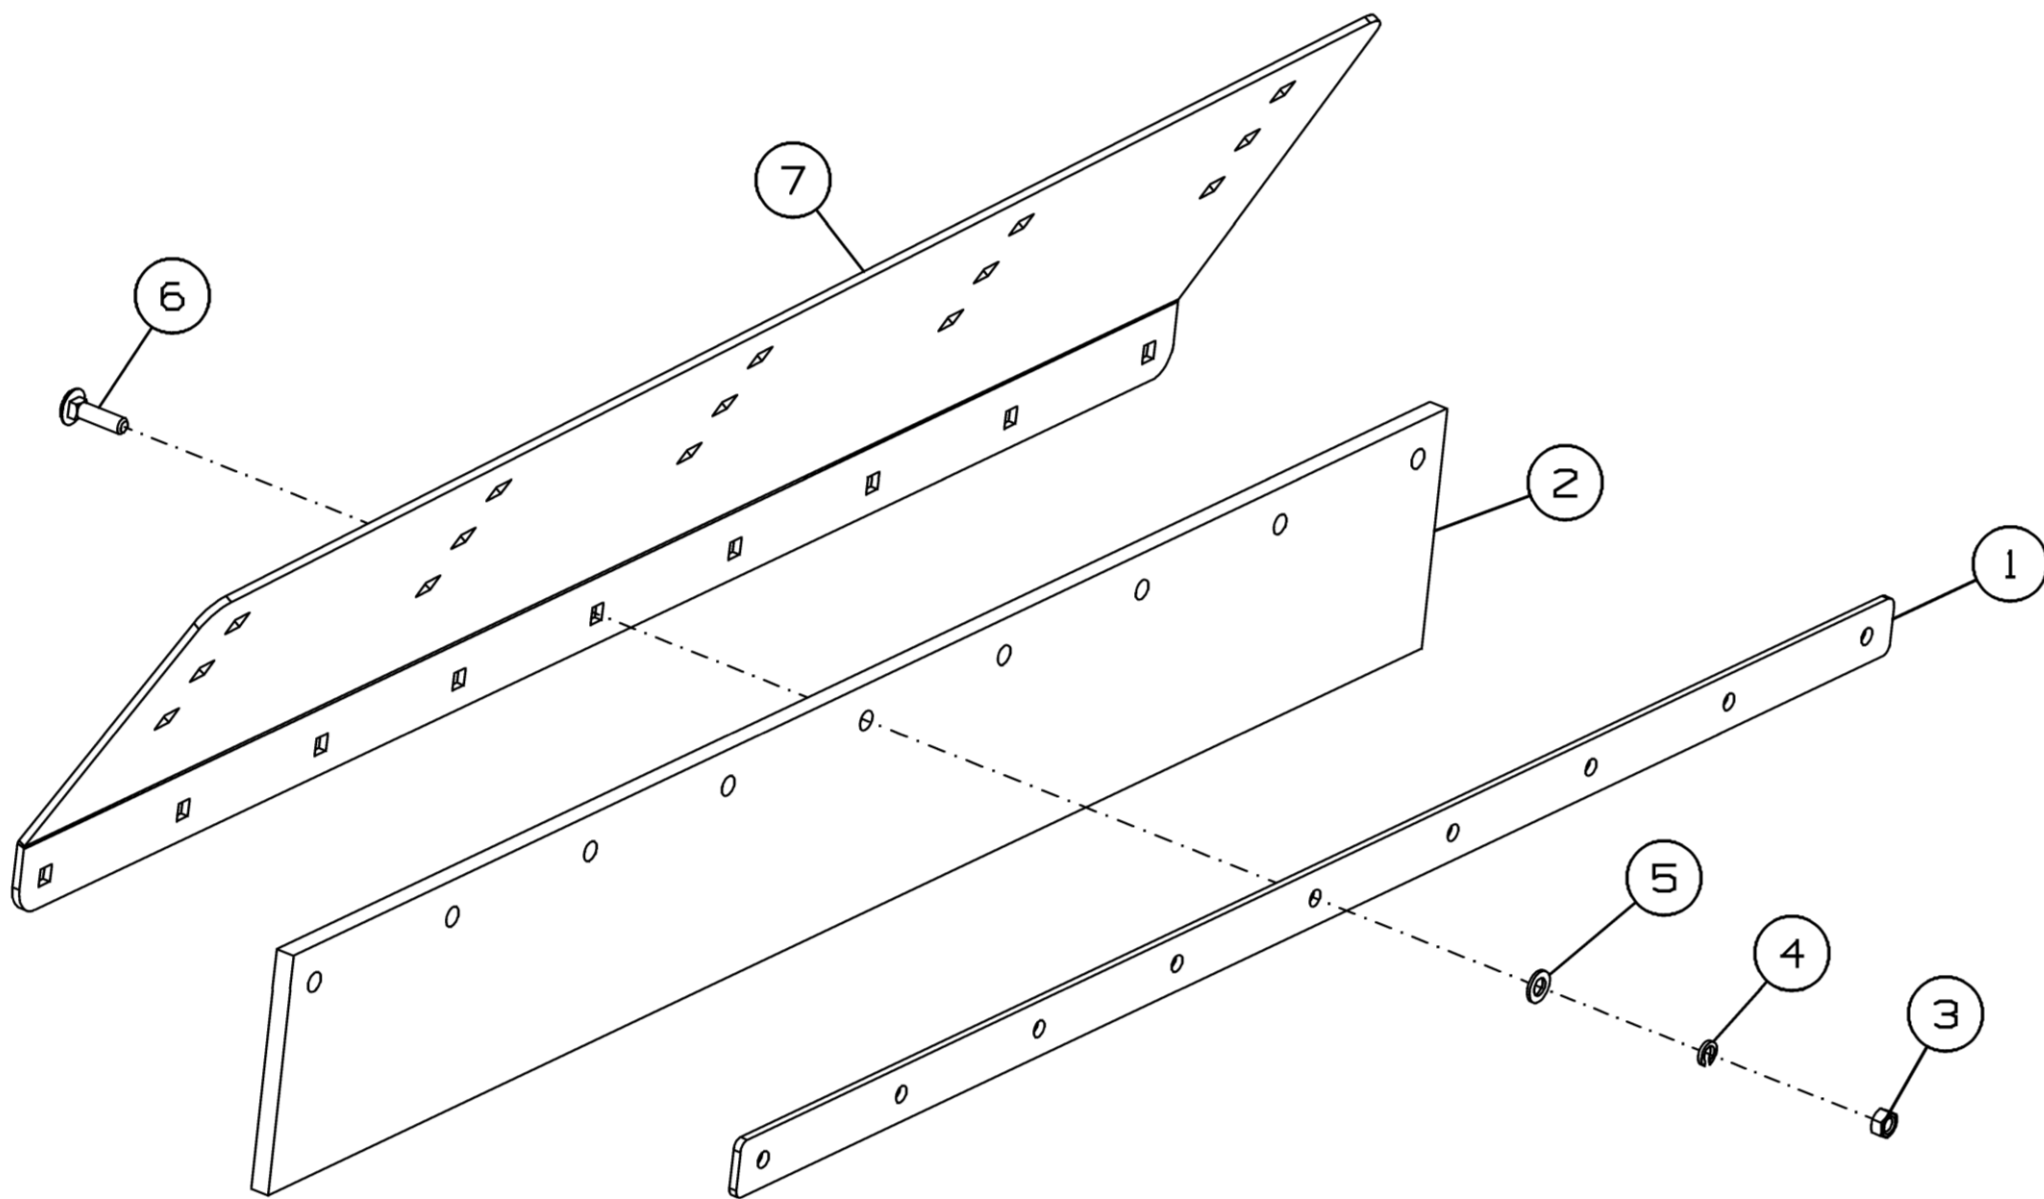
Дополнительный щиток валкообразователя GM-500R.06.01.140
